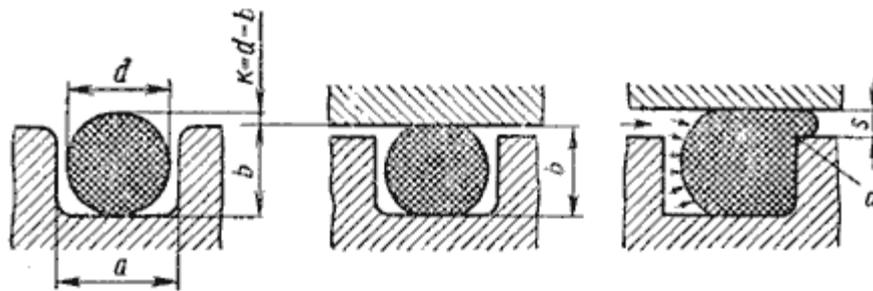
Схемы уплотнений резиновым кольцом круглого сечения
